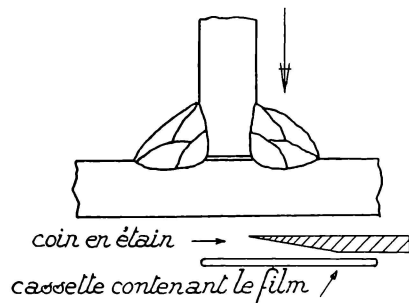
Radiographie d'une soudure d'angle.
